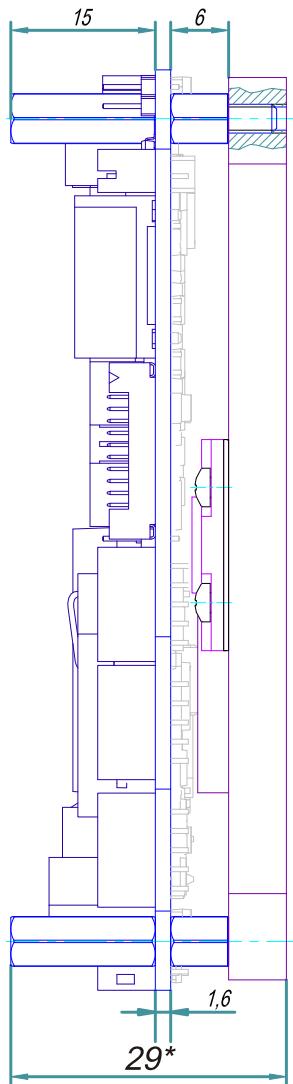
Габаритные размеры модуля (вид сбоку)
